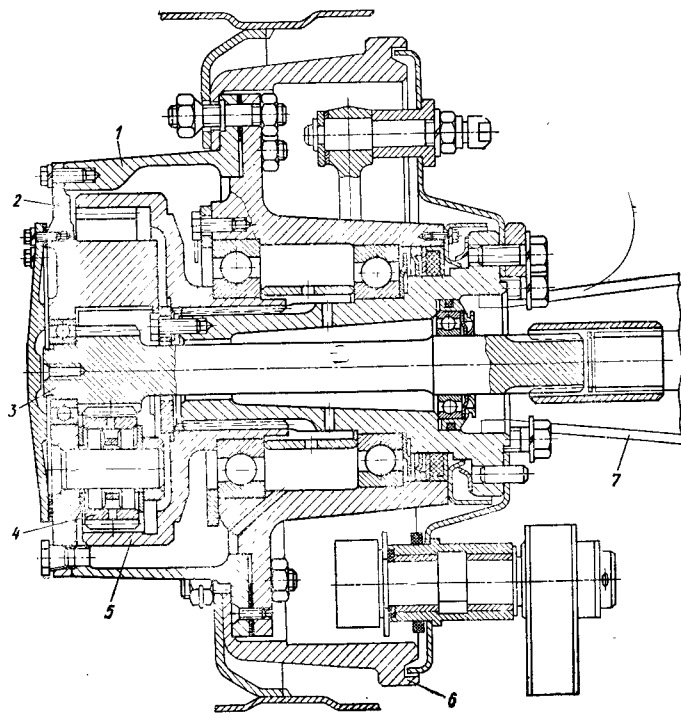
Планетарный колесный редуктор: 1 — ступица колеса; 2 — водило; 3 — солнечная шестерня с полуосью; 4 — спутник; 5 — неподвижная коронная шестерня; 6 — тормозной барабан; 7 — рукав заднего моста
